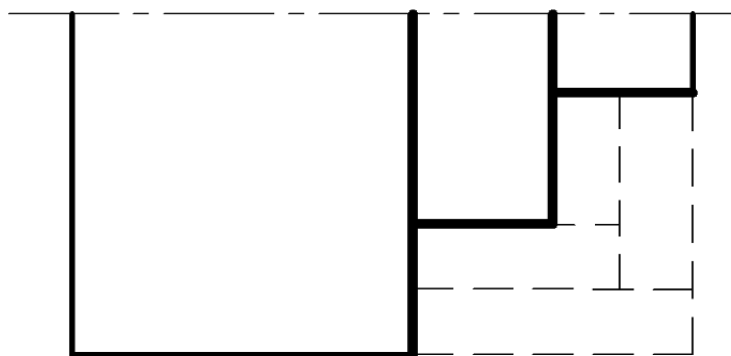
Схема удаления припуска заготовки в случае комбинирования направлений перемещений резца
